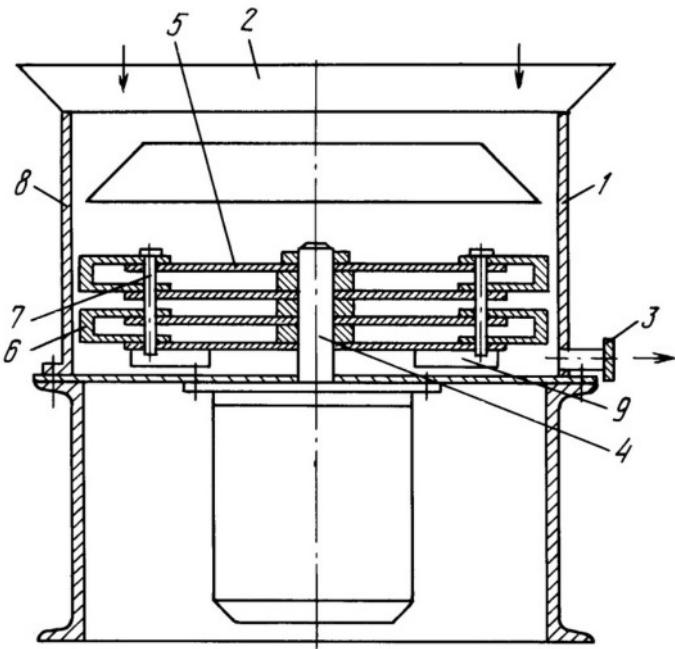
Общий вид вертикальной дробилки для кормов
